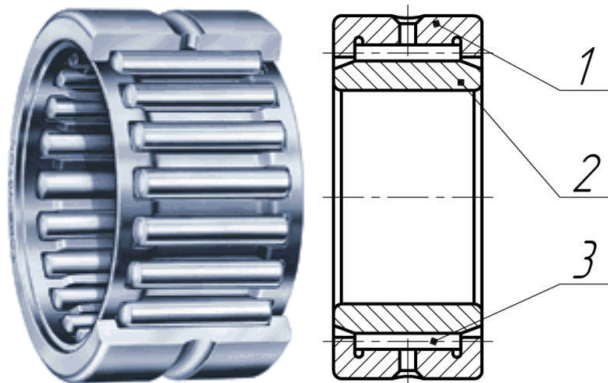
Конструкция роликового игольчатого подшипника:
